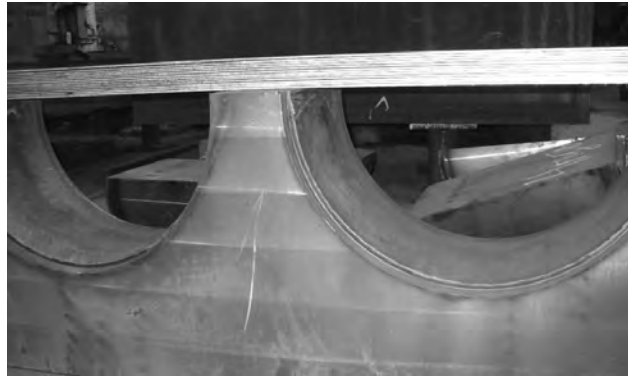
Заготовка корпуса подшипника толщиной 450 мм с вырезанными полукруглыми карманами
